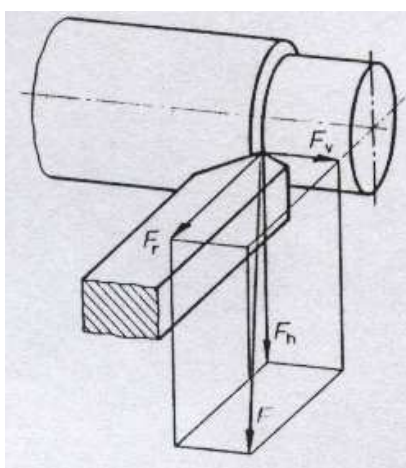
Fuerzas sobre la cuchilla¹⁹
